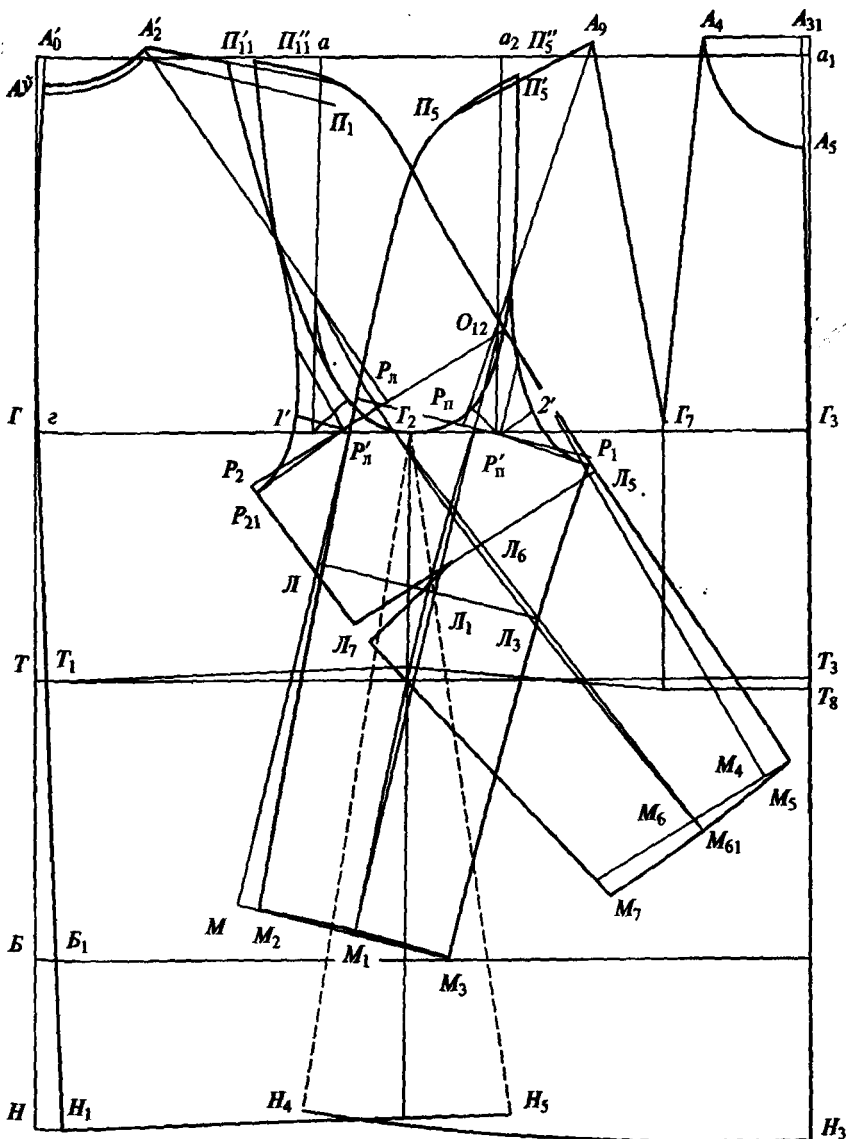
Чертеж конструкции изделия с рукавами покроя полуреглан
